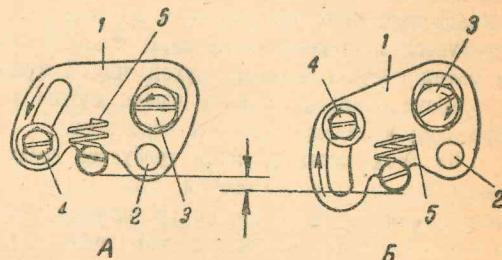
Схема приспособления для натяжения пружинки регулятора РРА-44:
